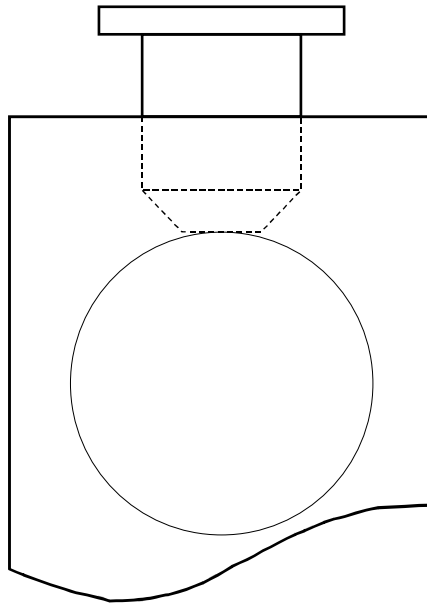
Draufsicht Teil 1: Tangentiales Berühren der Schraube mit dem Gegenstück
